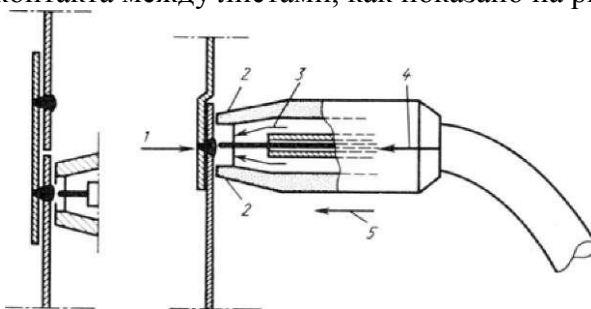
Точечная сварка тонких листов, один из которых выполнен с накладной лентой, а другой с отбортовкой: 1 - сварная точка; 2 - мундштук; 3 - защитный газ; 4 - размотка с выдержкой времени; 5 - небольшое усилие сжатия
